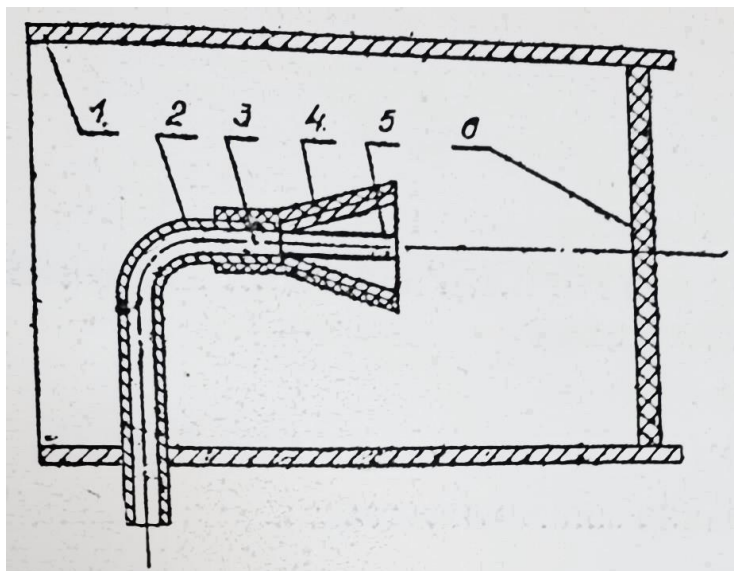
Генератор для получения омагниченной пены: 1 — корпус; 2 — раствороподводящий патрубок; 3 — распылитель с насадкой из немагнитного материала; 4 — постоянные магниты; 5 — прокладка из немагнитного материала; 6 — пакет сеток
